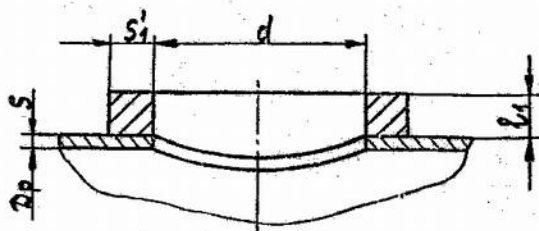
Расчетная схема соединения фланца со стенкой сосуда
